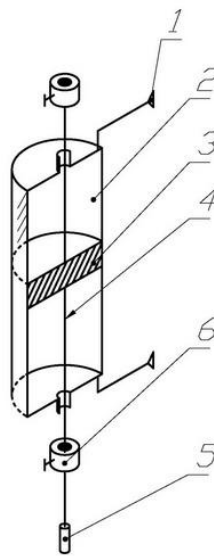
Молотковий механізм з приводом від пневматичного циліндру
